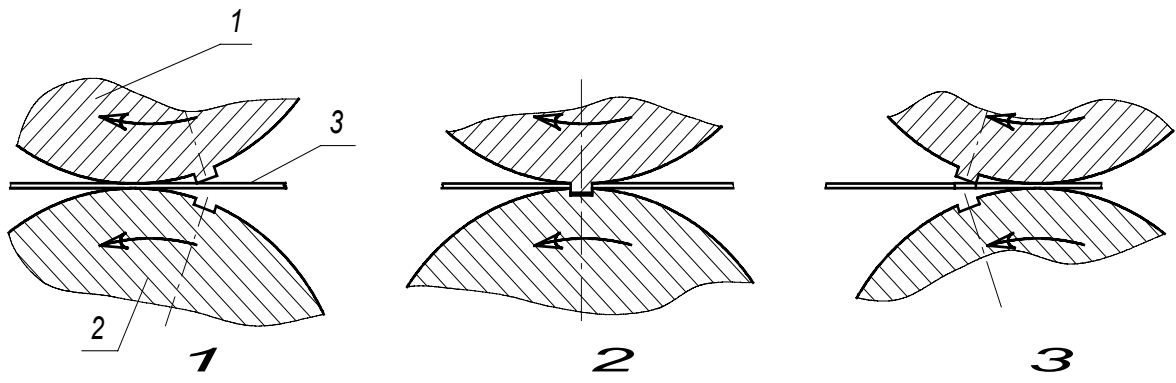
Схема валковой перфорации металлической полосы. валок с пуансонами; 2 - валок с матрицами; 3- перфорируемый металл.
